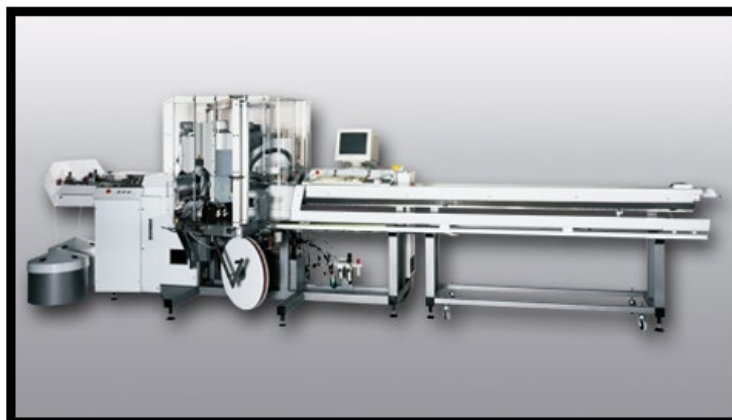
Equipamento de corte e cravação de fios de diferentes de secções [16].
